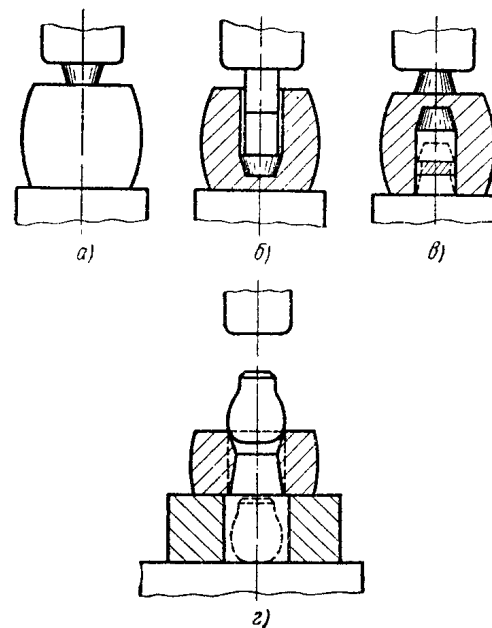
Схема прошивки и калибровки отверстия под молотом и прессом:
